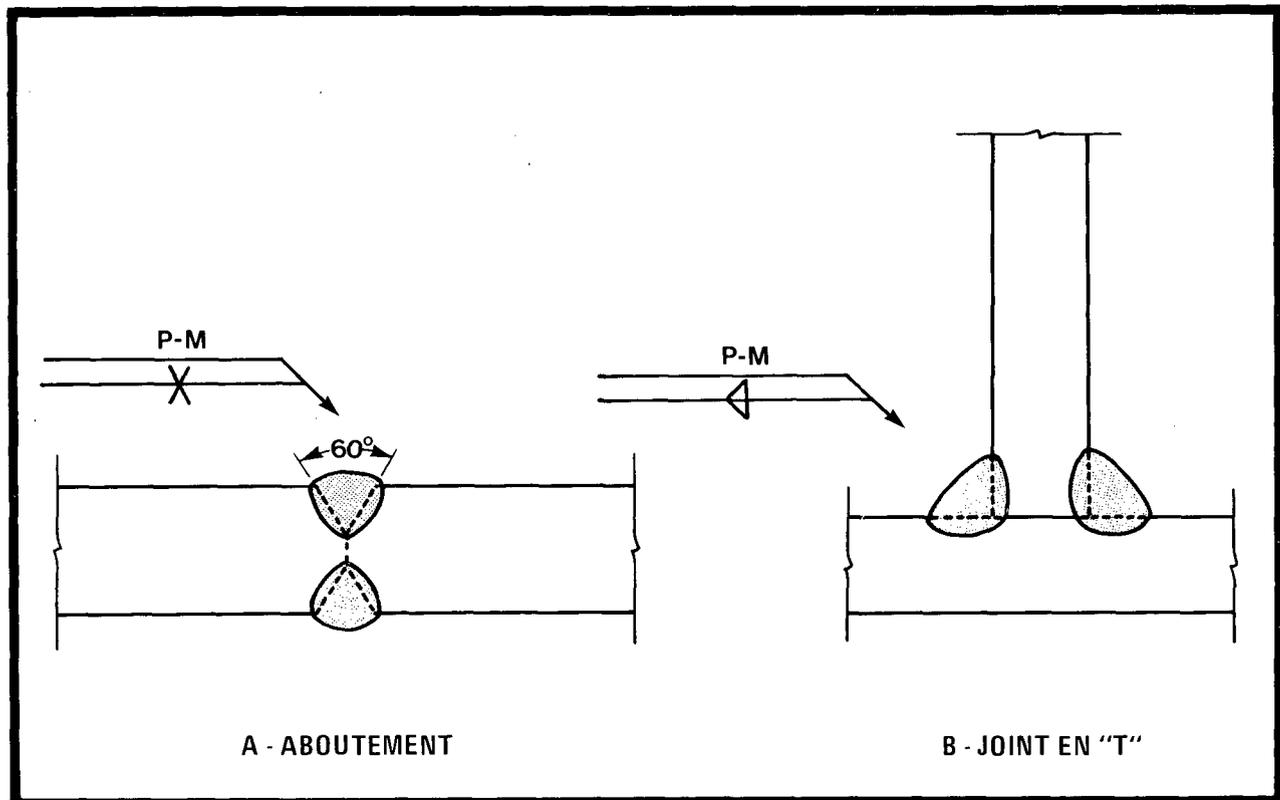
SOUDURE À PÉNÉTRATION INCOMPLÈTE
